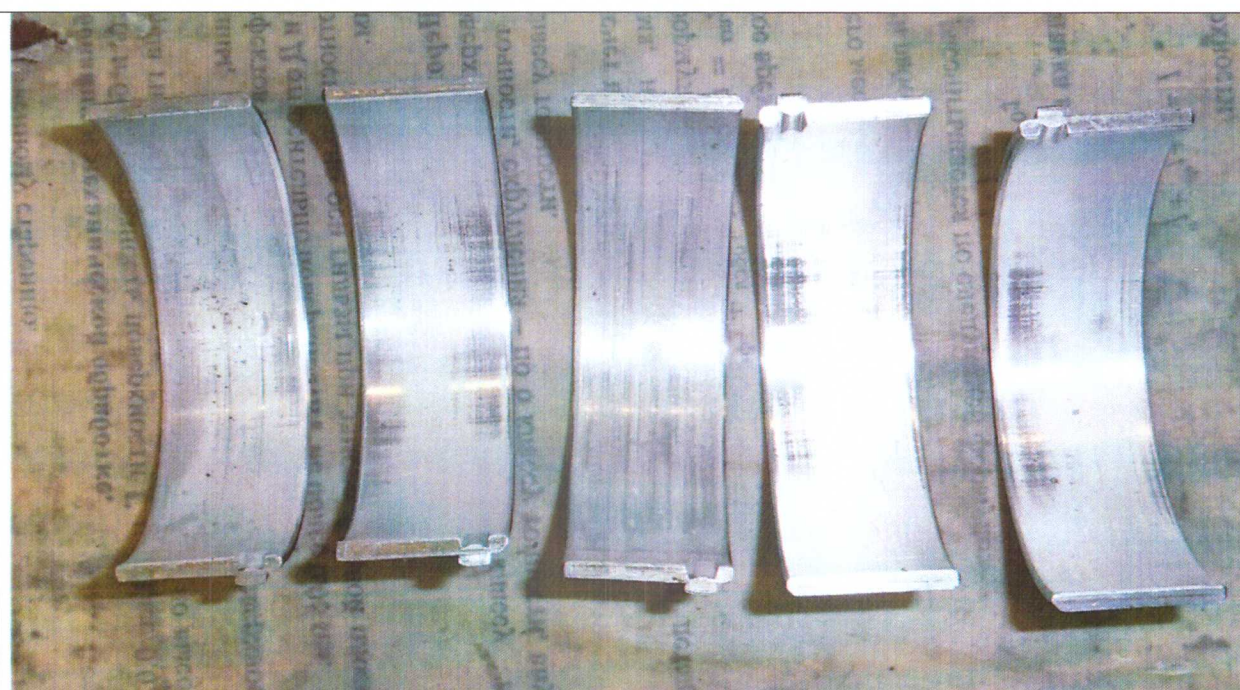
Внешний вид рабочей поверхности нижних вкладышей коренных подшипников коленчатого вала по окончании длительных испытаний двигателя при работе на базовом масле Castrol EDGE с добавкой нанокompозита Amortect PROOF
